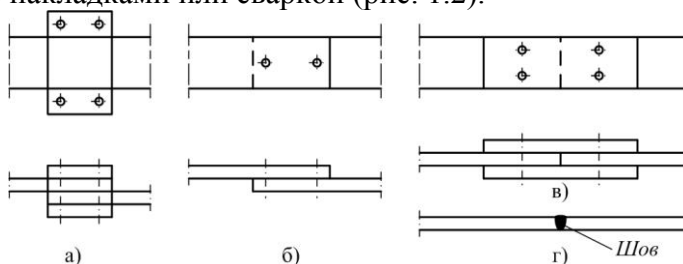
Жесткие контакты соединения шин: а – в нахлестку с накладками; б - в нахлестку болтами; в – в стык с накладками; г – сваркой
